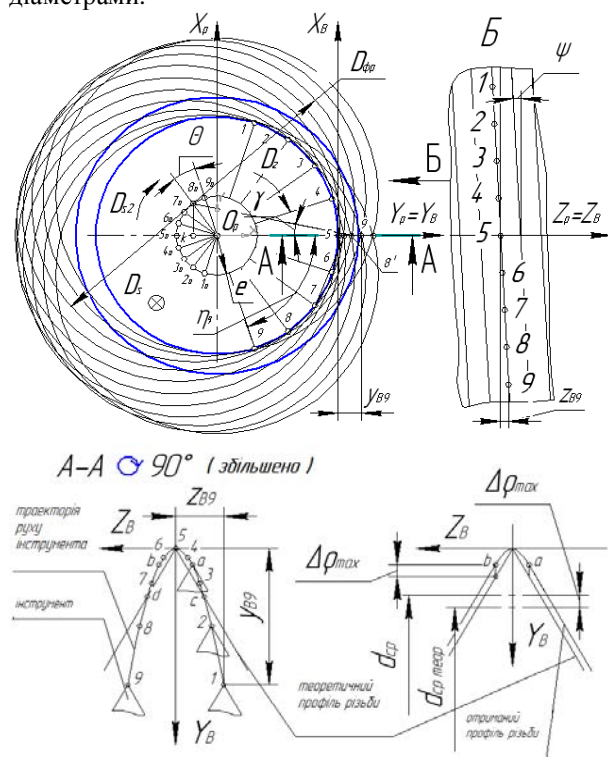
Схема формування зовнішнього різьбового профілю різьбофрезою
